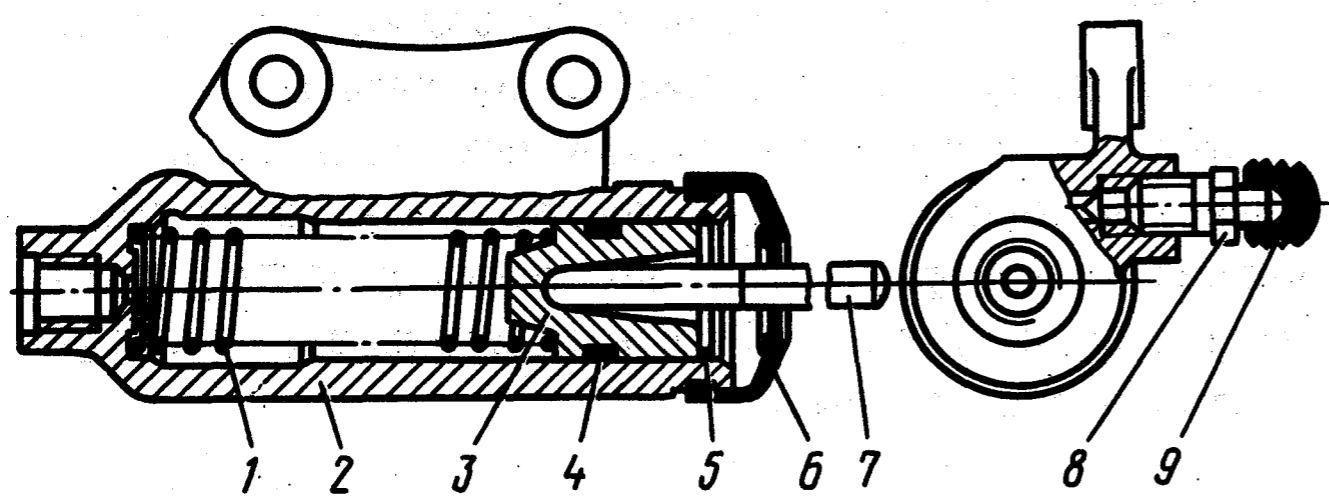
Рабочий цилиндр привода выключения сцепления:
